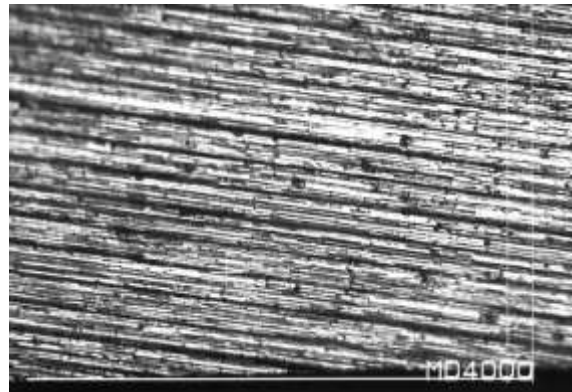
b. Das Gewinde des Messing-Teils nach dem Handschliff.
